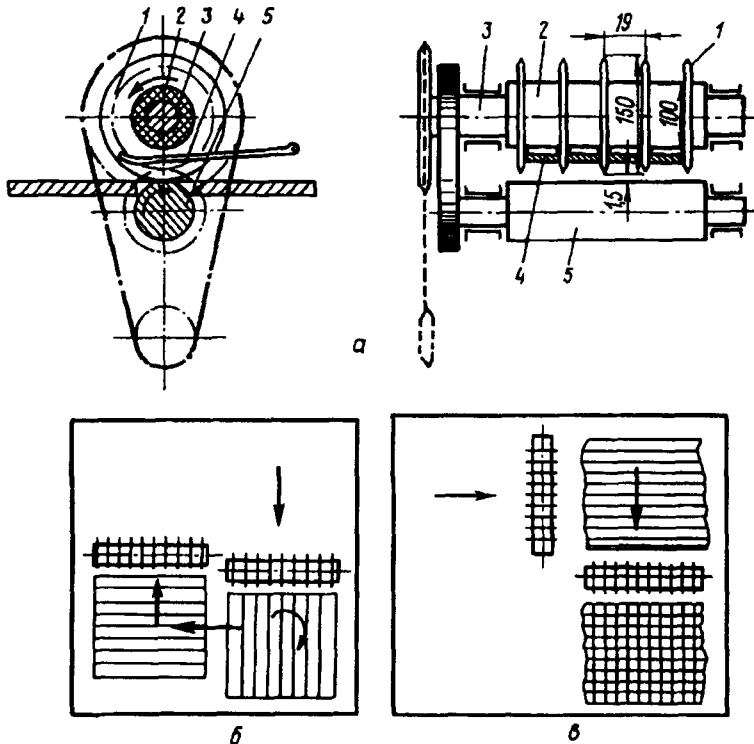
Устройство и расположение дисковых ножей в машине для резки пластов: а — устройство ножей; б — параллельное; в — перпендикулярное
